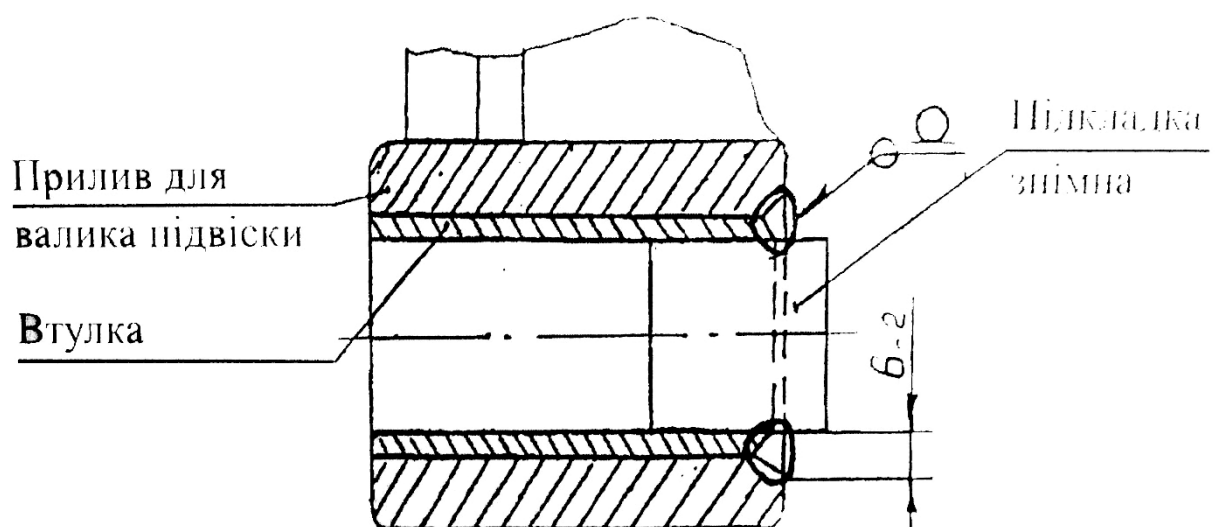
Схема приварювання втулки в розроблений отвір
